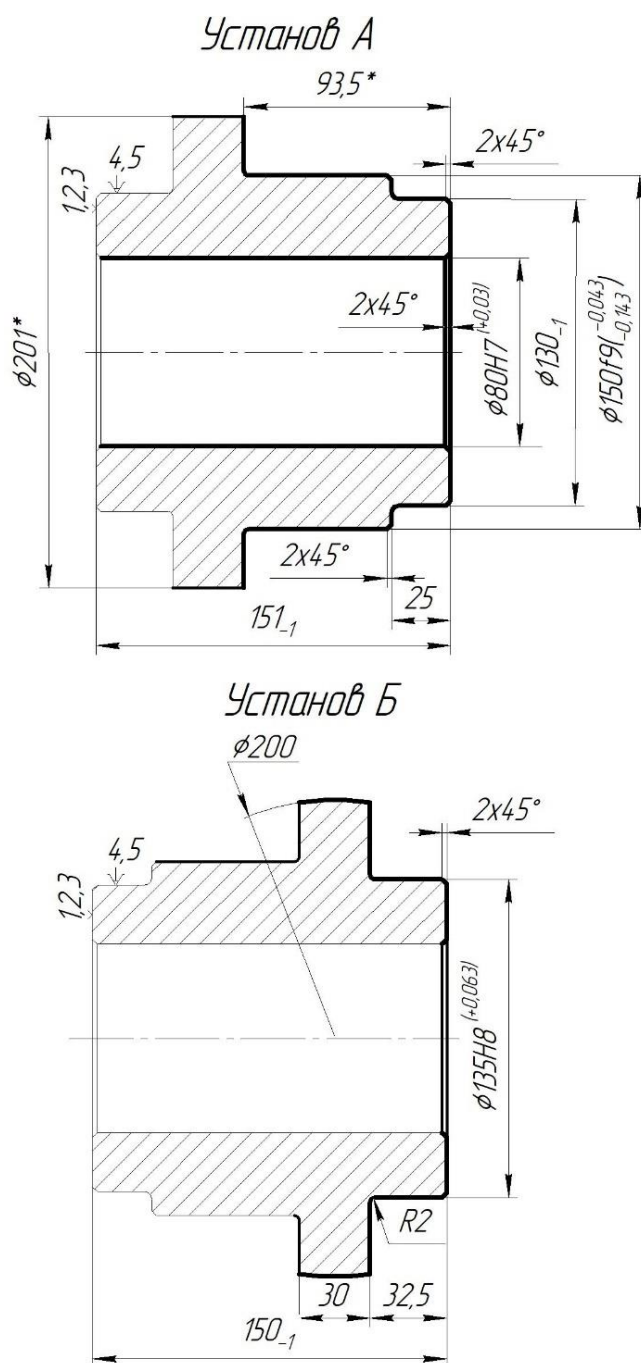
Схема базування деталі на операції 030 Токарна з ЧПК
